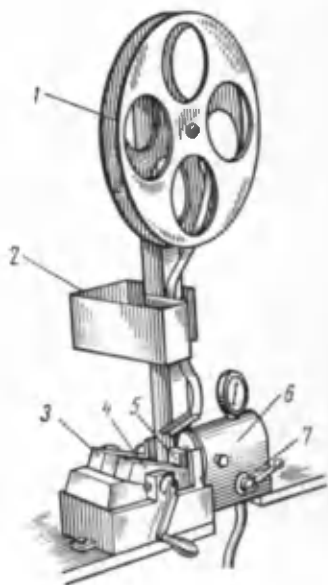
Машина для стягивания и бандажирования секций галетных элементов: 1 — бобина с полихлорвиниловой трубкой, 2 — ванночка с композицией, 3, 4 — сборочные щетки, 5 — шток, 6 — пневматический цилиндр, 7 — пневмоклапан
